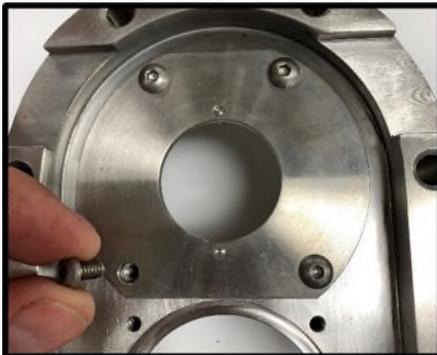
Herausnehmen der Schrauben des Dichtungsgehäuses
